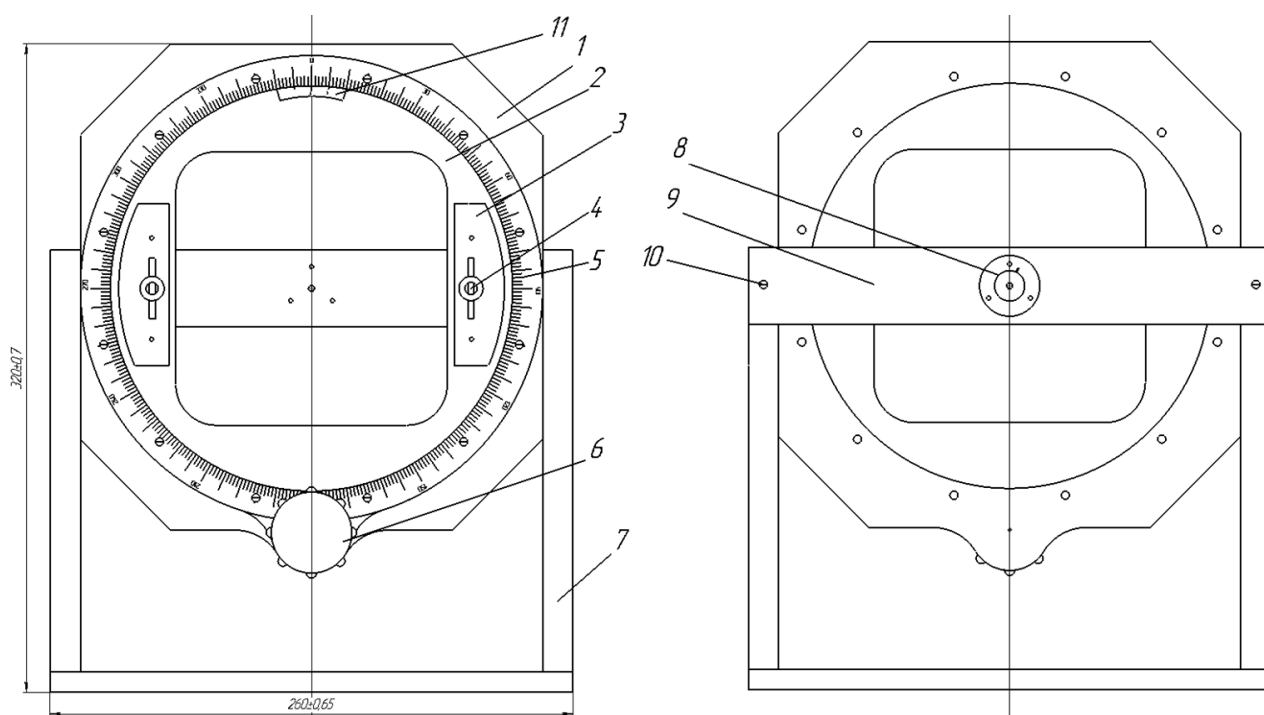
Чертеж общего вида задатчика угловых положений. Вид спереди, сзади: 1 – неподвижное кольцо; 2 – поворотное кольцо; 3 – прижимная планка; 4 – винт-барашек; 5 – шкала; 6 – ручка; 7 – основание; 8 – муфта; 9 – планка; 10 – винт; 11 – нониус
